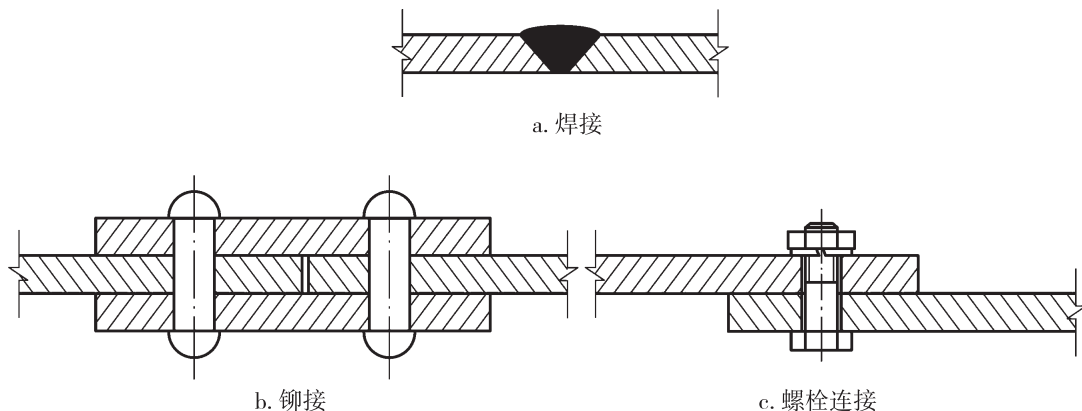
焊接、铆接和螺栓连接示意图
